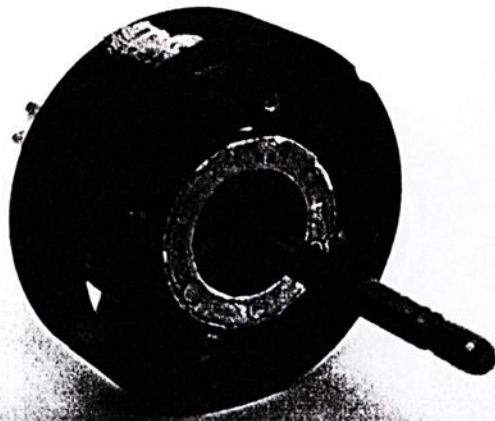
CONJUNTO ROTOR - ESTATOR
